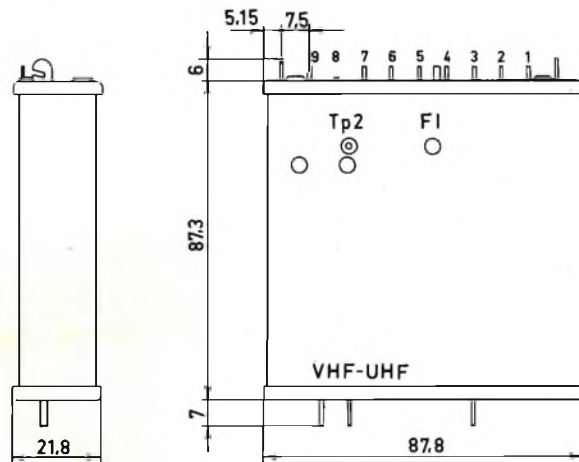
Dimensioni di ingombro del sintonizzatore a «varicap» VHF-UHF- serie 16000: si noti la diversa disposizione del collegamento di antenna, che in questo caso risulta unico.
